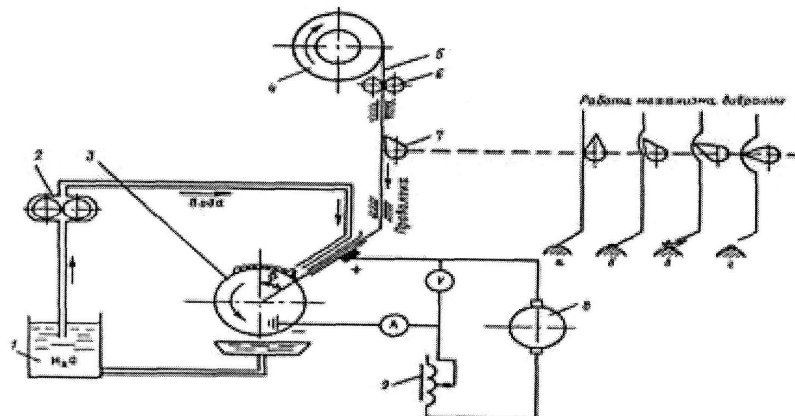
Схема установки для вібродугового наплавлення деталей:
